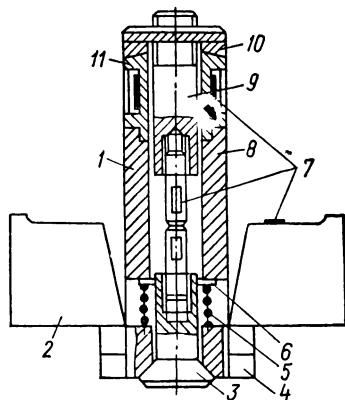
Устройство для реализации ударного растяжения образца с кольцевой трещиной с возможным размещением датчиков нагрузки:
